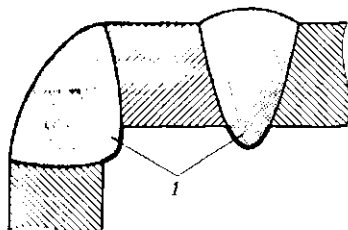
Избыточная выпуклость 1 корня шва углового и стыкового сварных соединений
